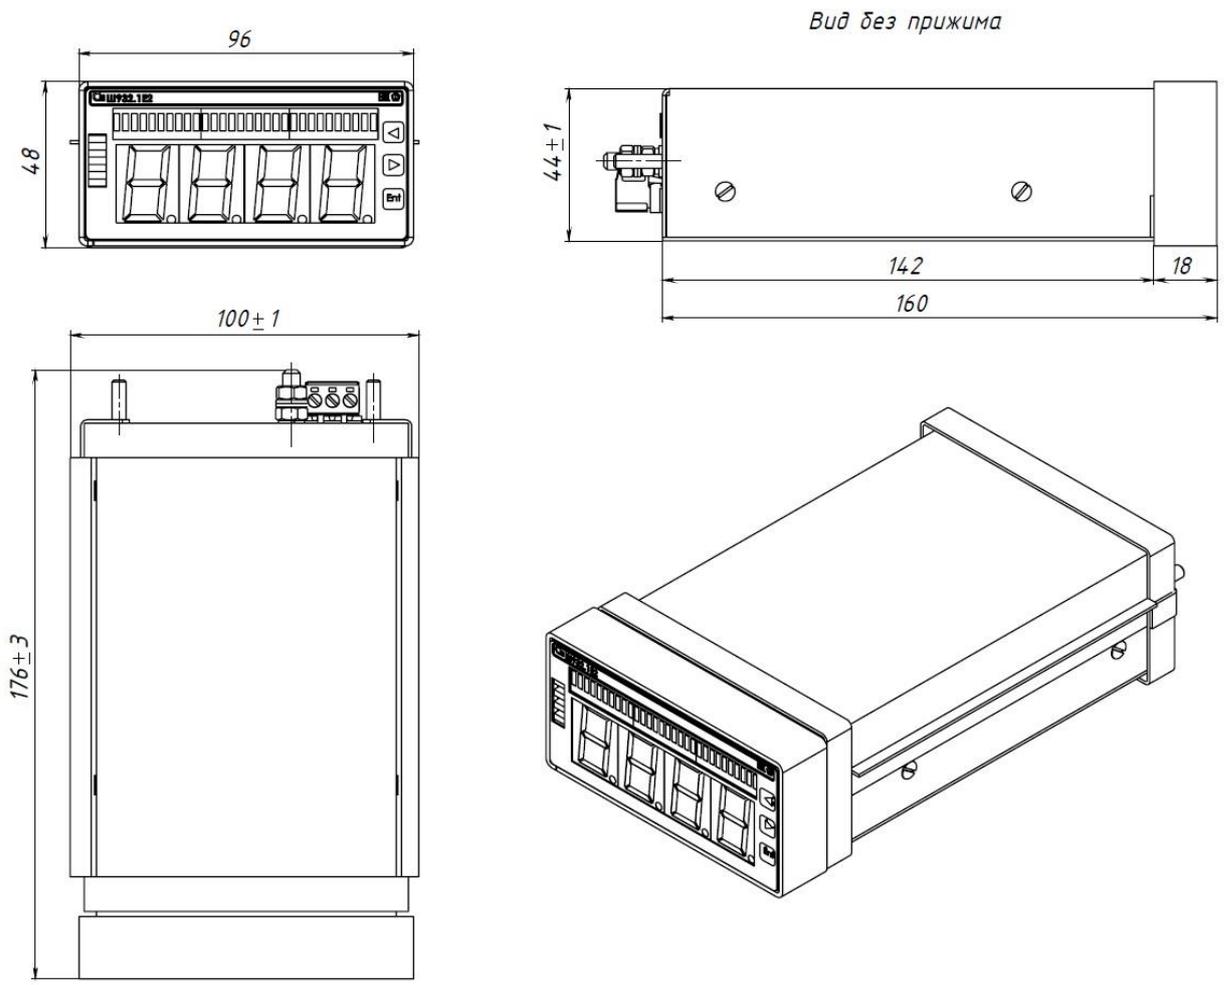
Габаритные и установочные размеры прибора Ш932.1Е2
